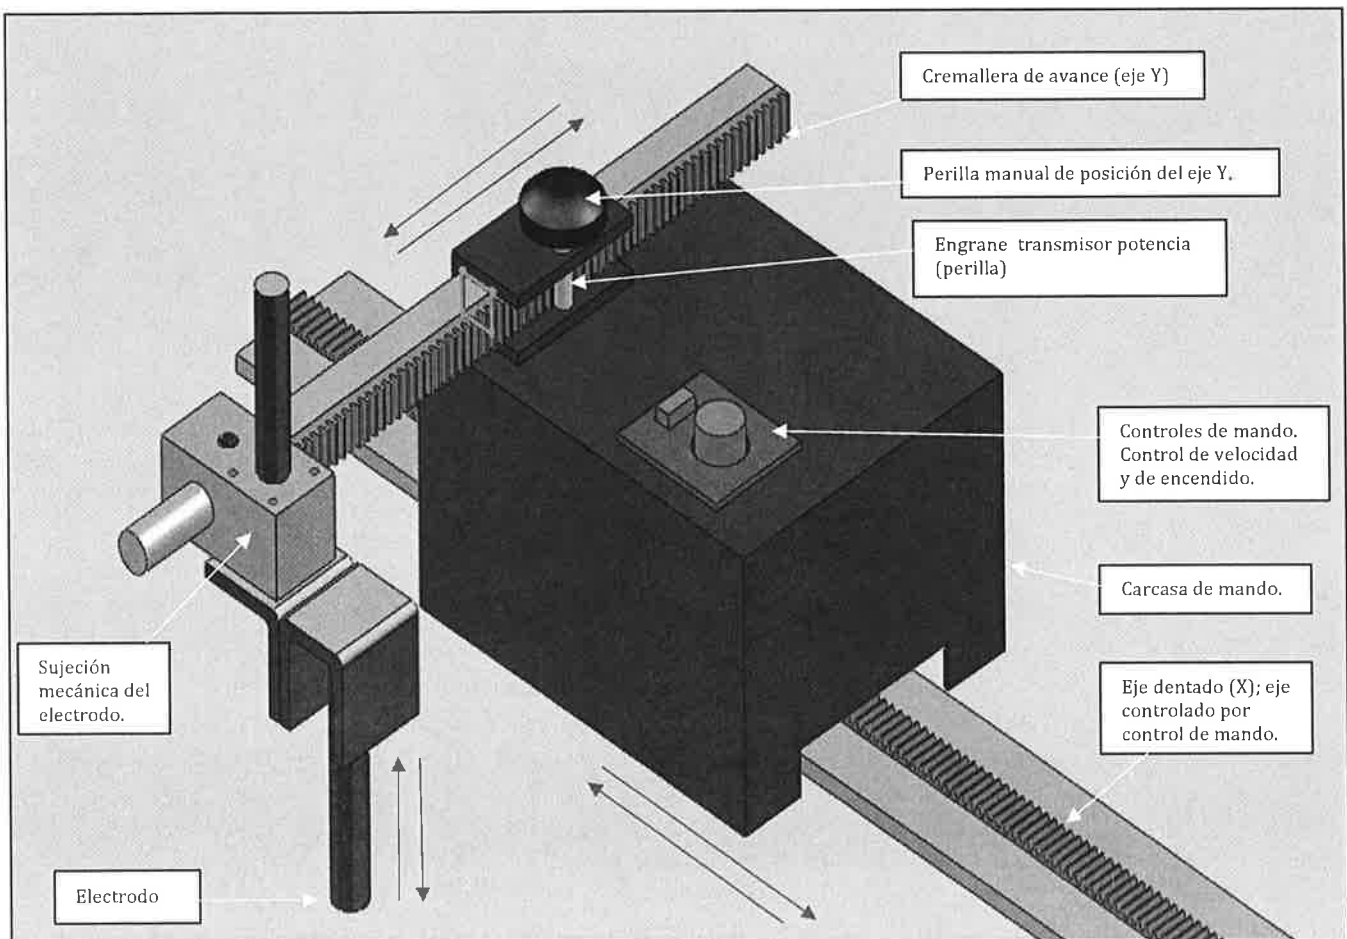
Funcionamiento del equipo de soldadura antes del proyecto.
